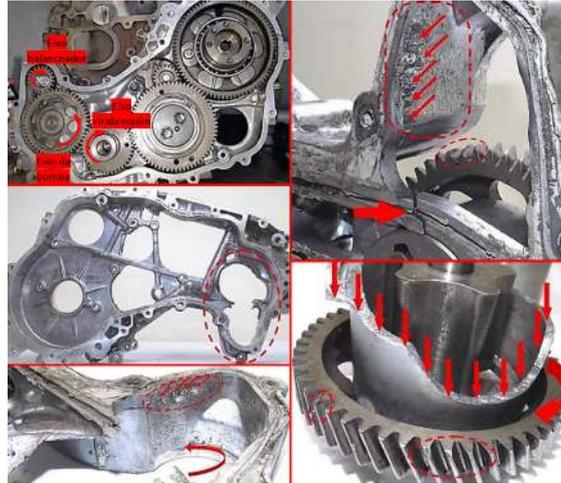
Quebra da carcaça da bomba do tipo conjunto engrenado:
